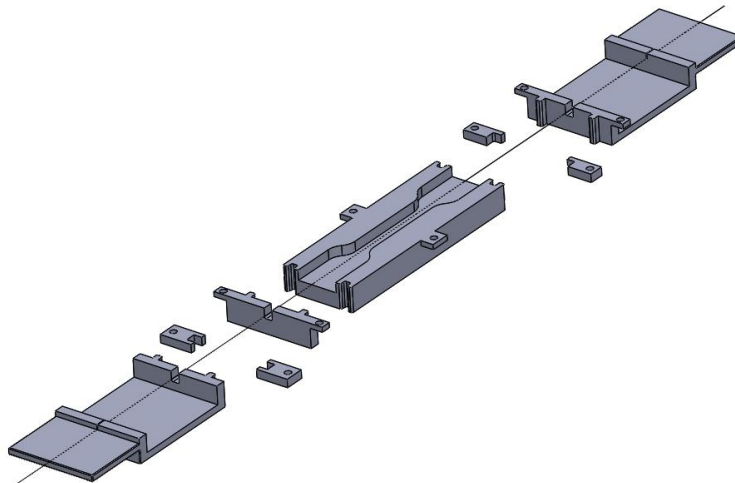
Moule en impression 3D pour insérer un capteur à réseau de Bragg au sein d'une éprouvette type "haltère" par moulage
